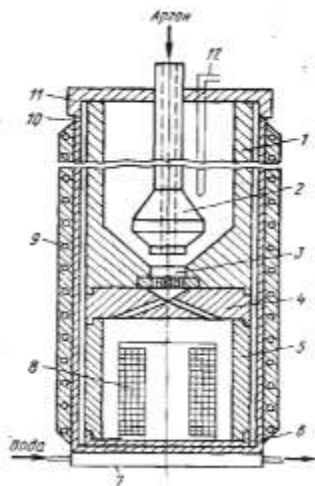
Схема установки для получения КМ пропиткой: 1 - графитовый тигель; 2 - запорный плунжер; 3 - фильтр; 4 - пробка с коллектором и питателями; 5 - заливочная камера; 6 - дно; 7 - холодильник; 8 - заготовка из армирующего материала; 9 - нагреватель; 10 - контейнер; 11 - крышка; 12 - термopара
